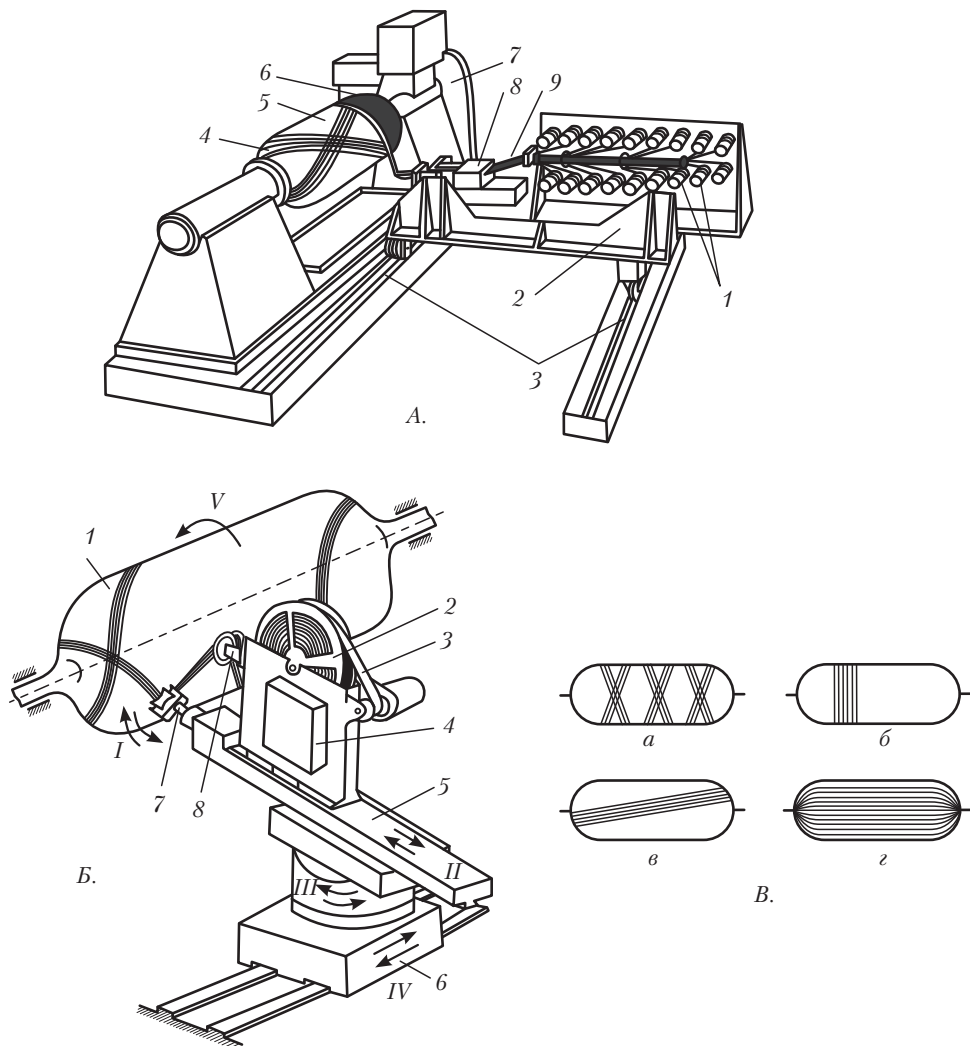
Схемы изготовления изделий из ВПКМ намоткой [1]:
